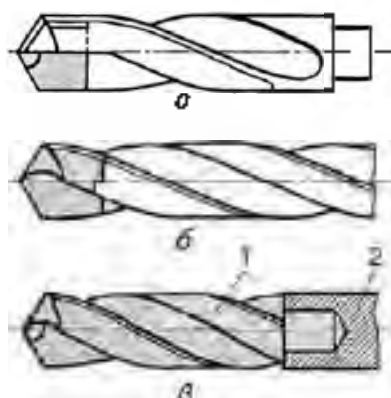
ТИВЕРДОСПЛАВНІ СВЕРДЛА.
